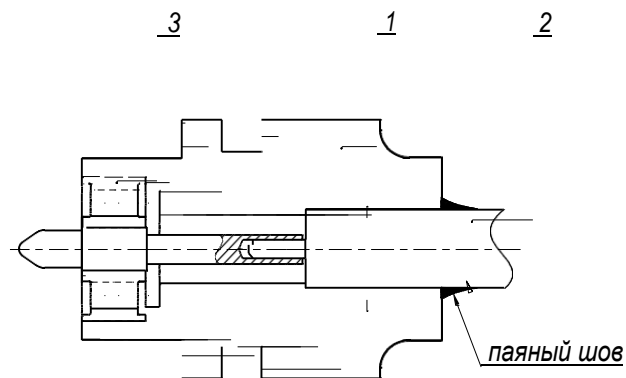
Запрессовка диэлектрической опоры в кабельный соединитель
